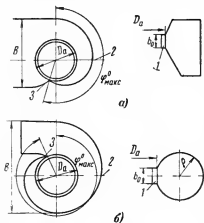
Схемы спиральных камер. а - бетонная тавровой сечения; б - металлическая круглого сечения; 1 - колонна статора; 2 - ось турбины; 3 - зуб спирали.
